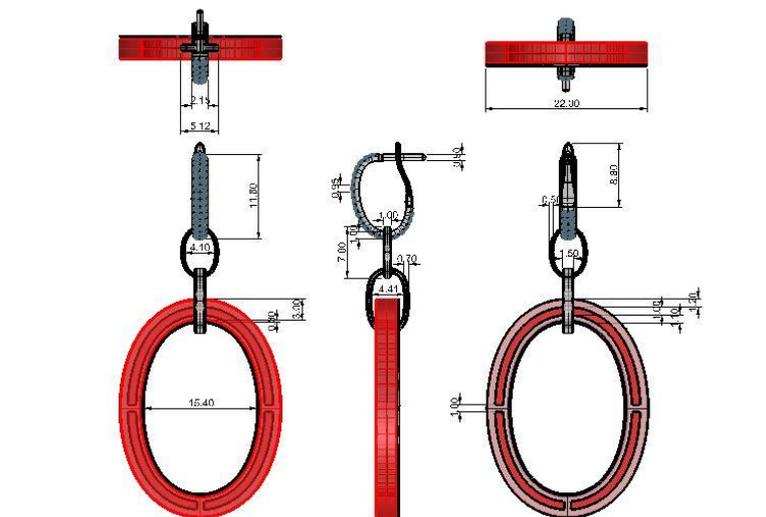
DESENHO TÉCNICO DO BRINCO A SER COPIADO
